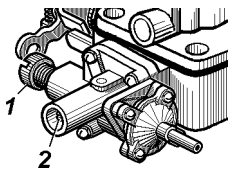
Корпус смесительных камер карбюратора (фрагмент):
